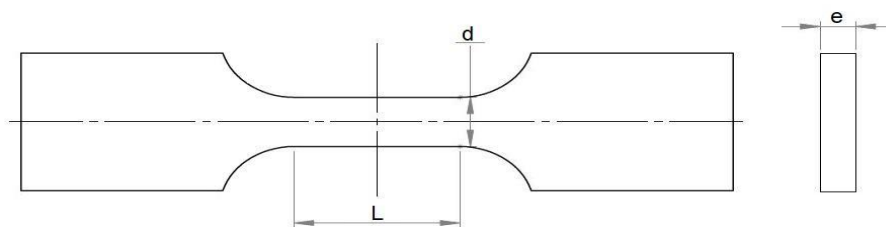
Desenho técnico do corpo de prova de tração com dimensões genéricas.
